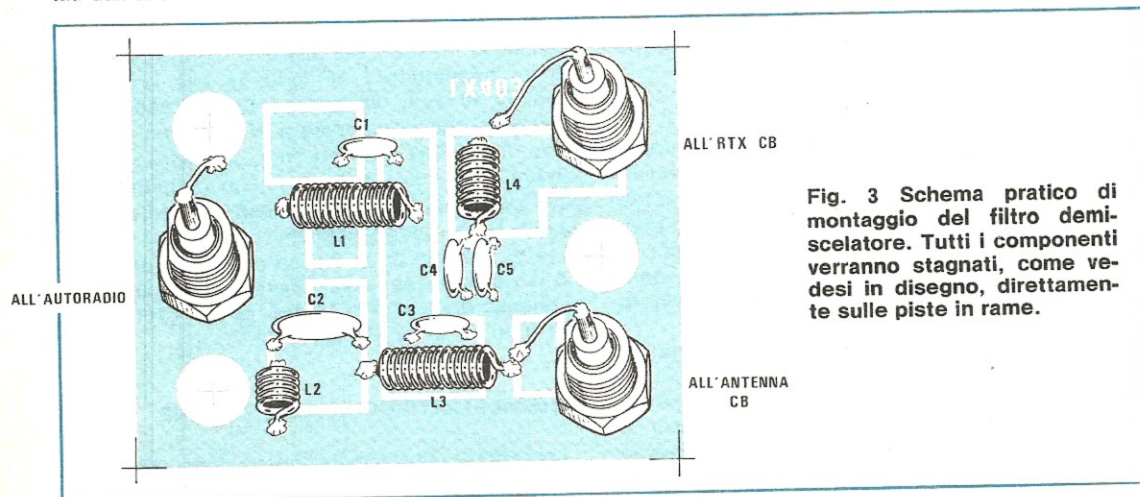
Schema pratico di montaggio del filtro demiscelatore. Tutti i componenti verranno stagnati, come vedesi in disegno, direttamente sulle piste in rame.
